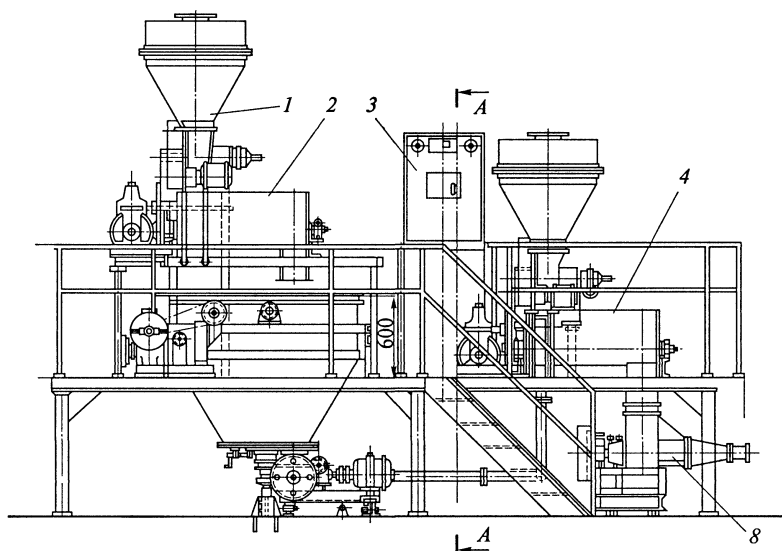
Агрегат для непрерывного приготовления и натирки бараночного теста
